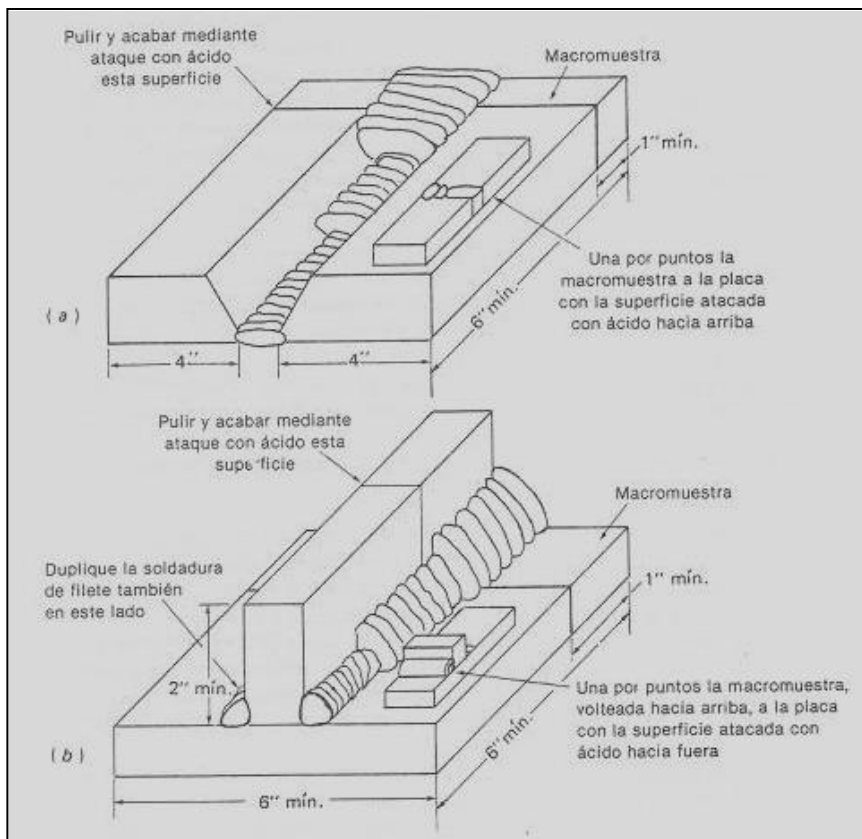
Normas relativas a la mano de obra de aplicación. a) Soldaduras de ranura; b) soldaduras de filete
